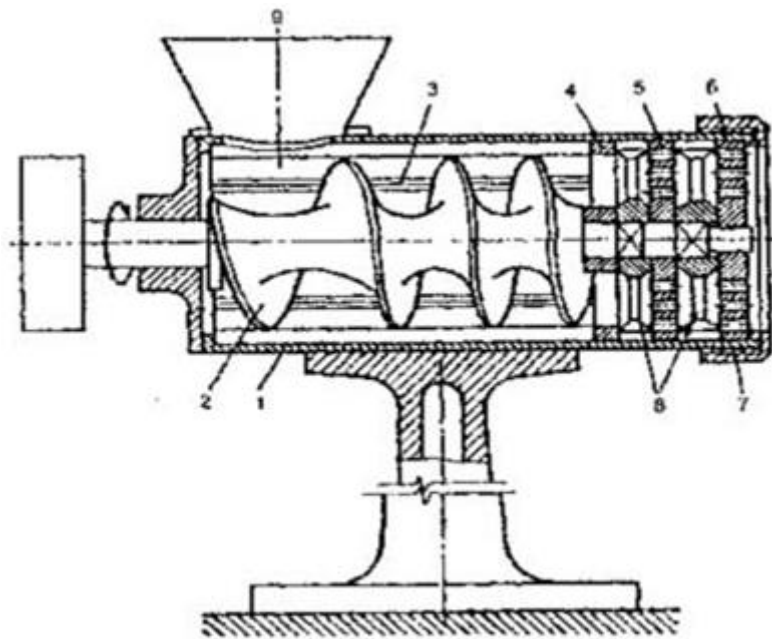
Принципова схема вовчка: 1 – робоча камера; 2 – шнек; 3 – ребра; 4 – підрізна решітка; 5,6 – ножові решітки; 7 – затяжна гайка; 8 – хрестоподібні ножі; 9 – чаша завантаження.
